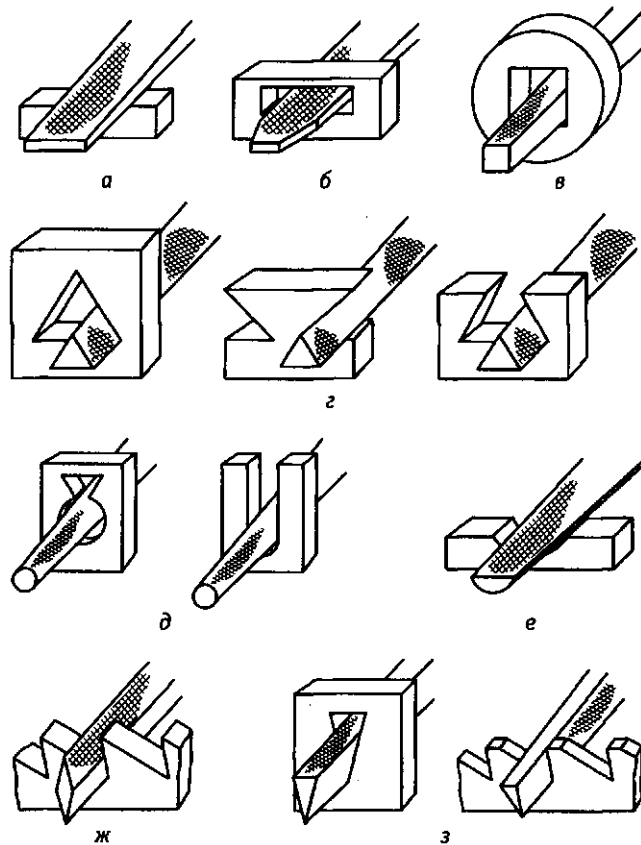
Форма поперечного сечения напильников и обрабатываемых поверхностей:
